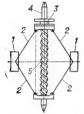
Кинематическая схема механического центробежного тахометра: 1— грузы; 2— рычаги; 3— скользящая муфта; 4— вал; 5— пружина.
